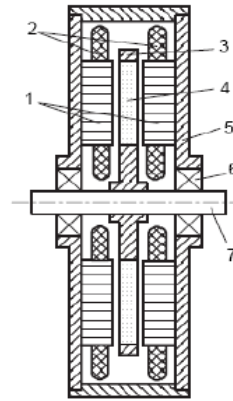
Descriptif de la machine à flux axial stator externe [16].
